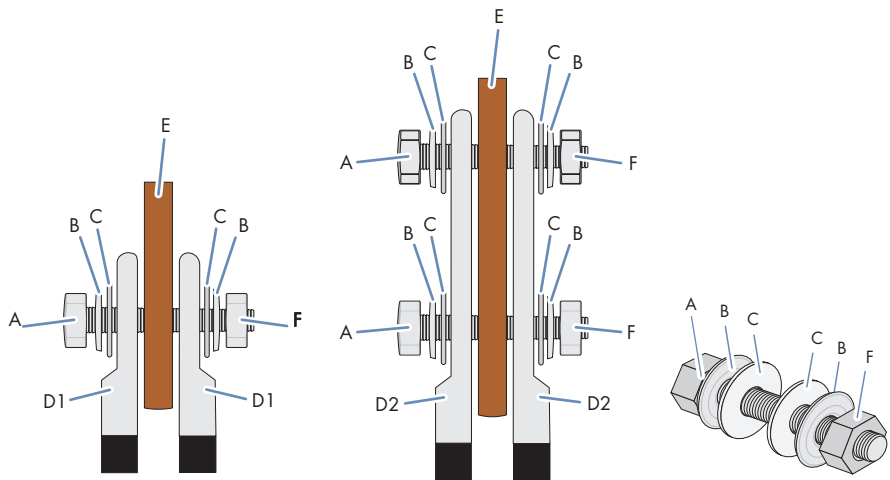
Estrutura da ligação de 2 terminais do cabo.
